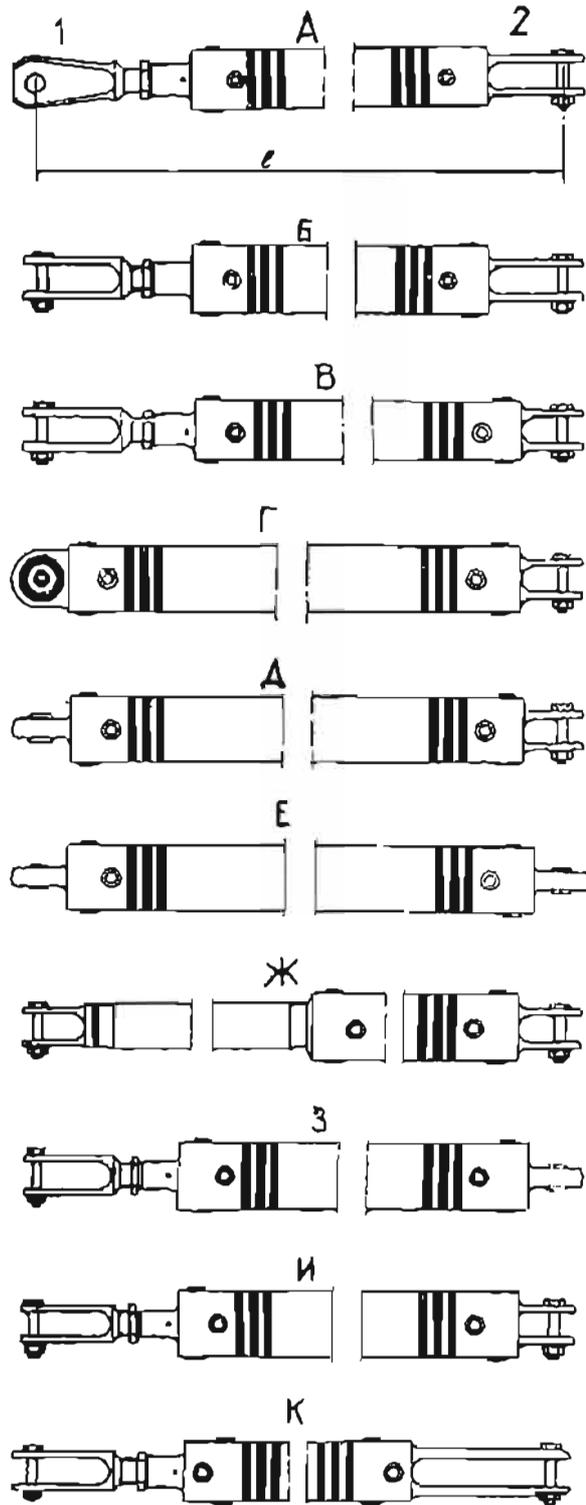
Kennzeichnung der Steuerstangen des Höhenruders
